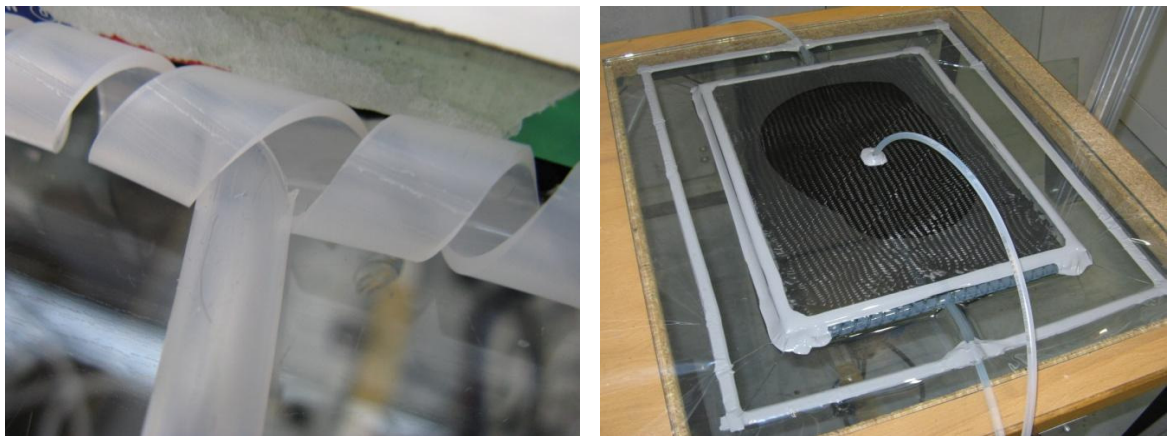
Befestigung der Vakuumschläuche (links), Aufbringen der Vakuumfolie (rechts)
